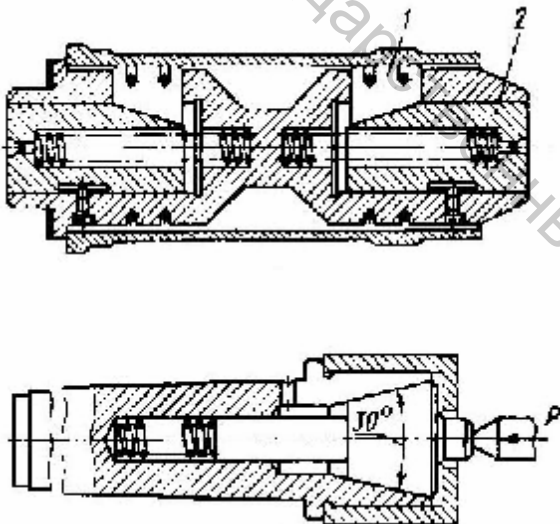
Консольная цанговая и кулачковая центровая оправки
